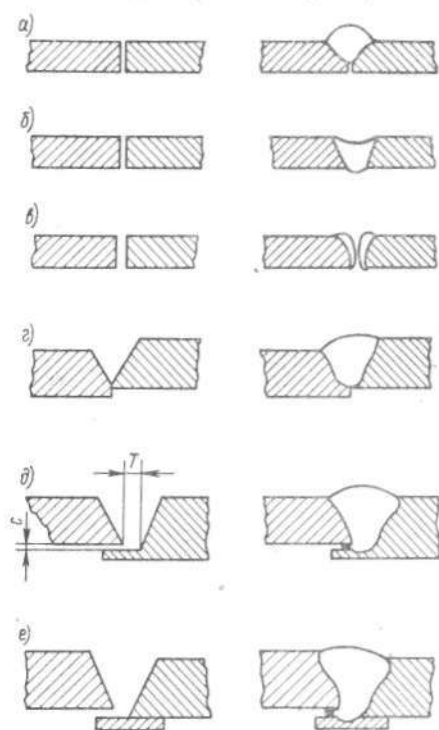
Влияние точности сборки деталей на качество сварки.
